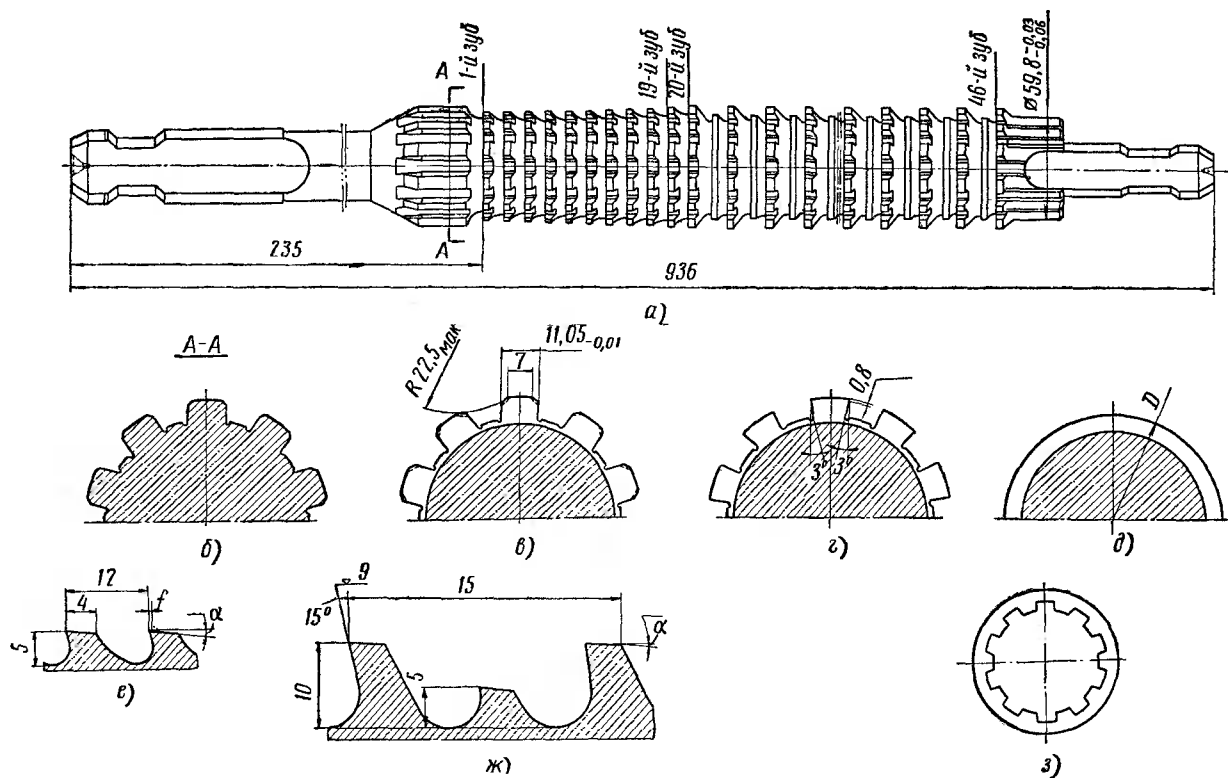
Шлицевая калибрующая протяжка с переменной схемой резания:
